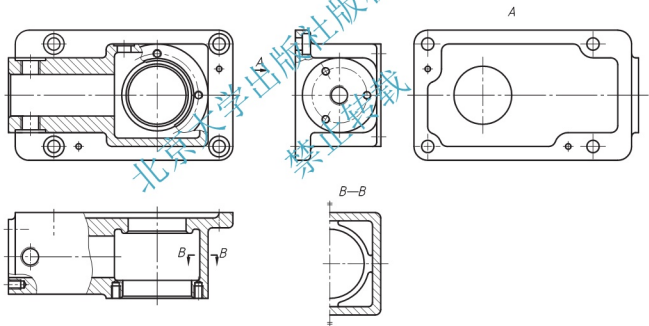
由卧式柱塞泵装配图分离并补全图线的泵体零件图
